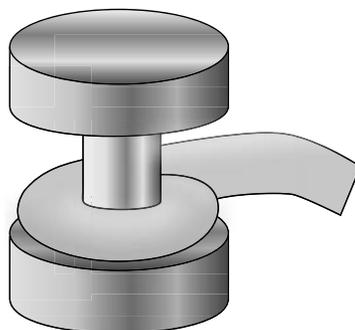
■ Conductor de componente fijado en un borne antes de soldarlo. Está enrollado alrededor del borne en $\frac{3}{4}$ de vuelta.
